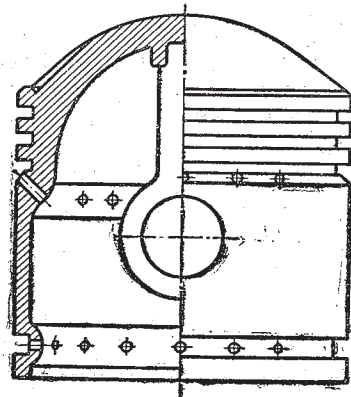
Рекомендуемое расположение колец на поршне спортивного двигателя
